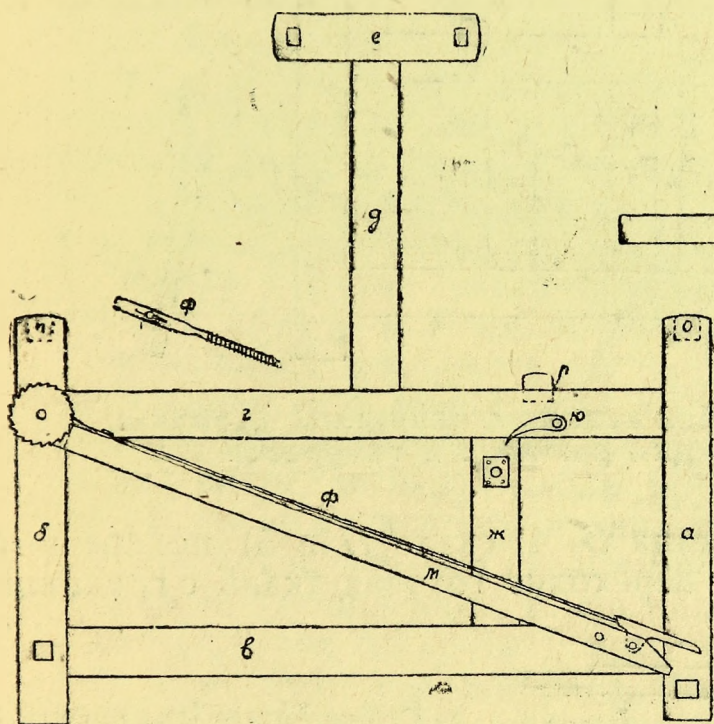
Правый бок финляндского станка с внутренней стороны и общий вид прибора *М* для спуска основы с заднего навоя, *ф* — вид защелки сверху.
